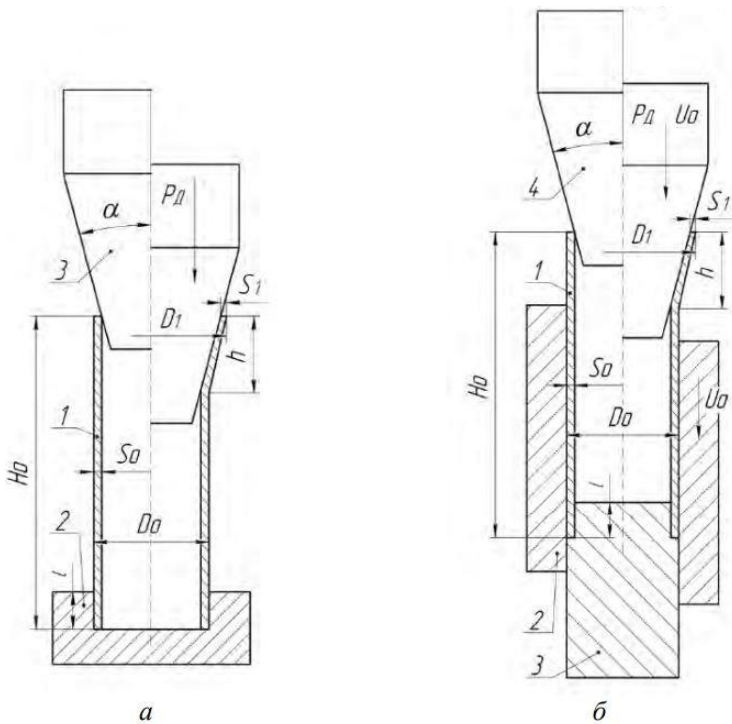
Схеми роздачі трубчастих заготовок:
